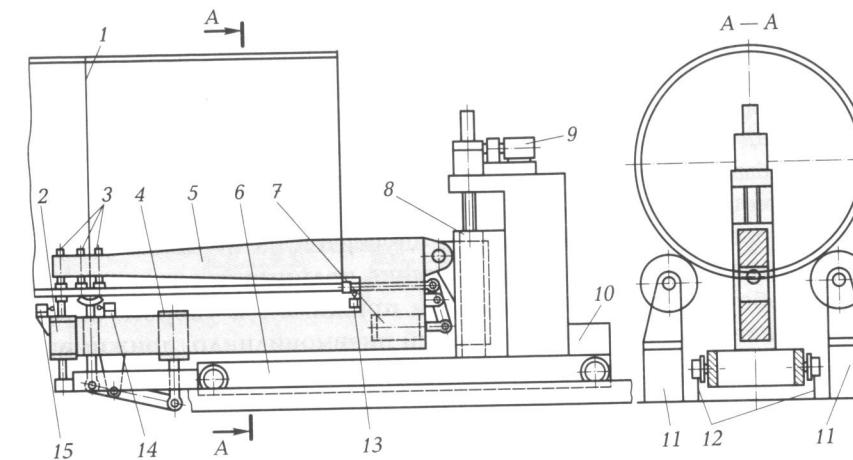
Установка для сборки обечаек по кольцевым стыкам:
